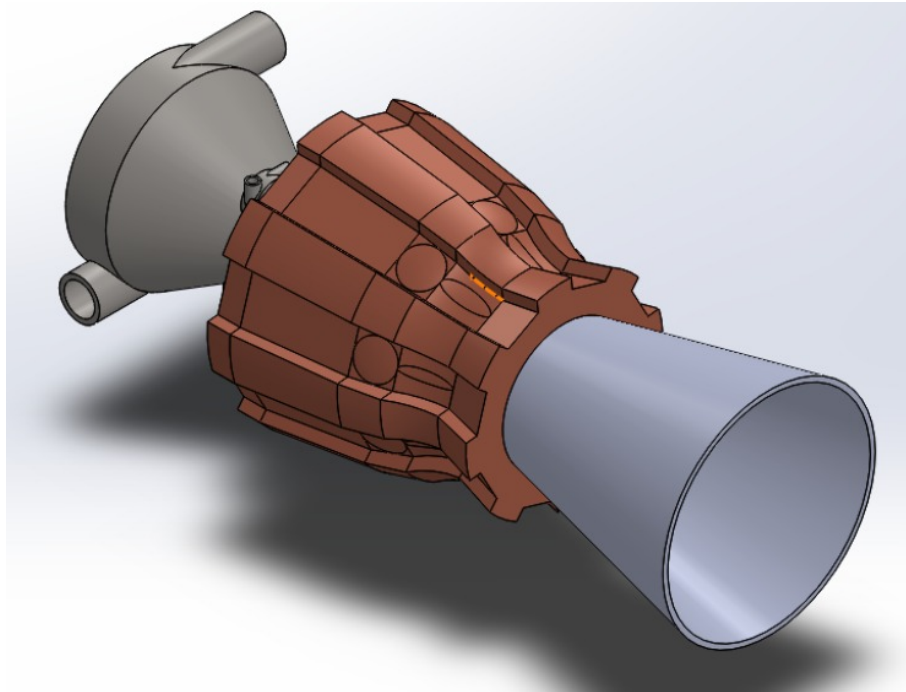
Vista Isométrica da Montagem do Motor com Bocal, Câmara de Combustão e Injetores.
